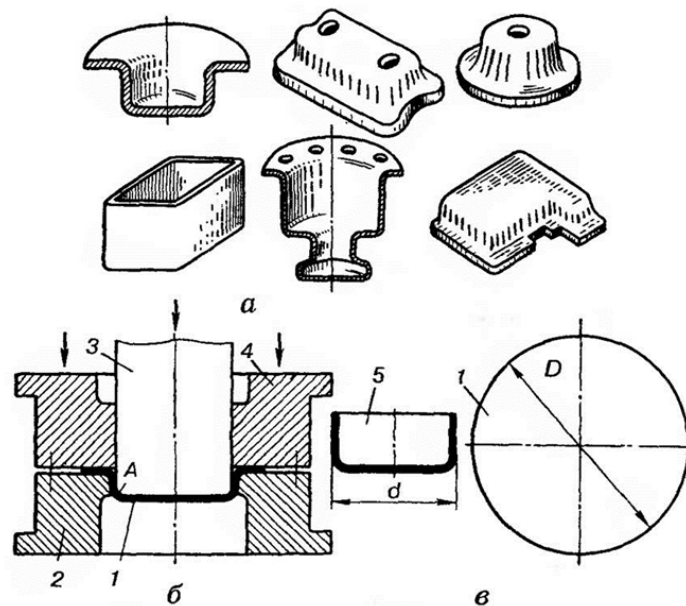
а) - Різні деталі отримані витяжкою. б) - Схема операції витяжки: 1 – заготовка, що деформується; 2 – матриця; 3 – пуансон; 4 – притискач; 5 - деталь; в). заготовка.
